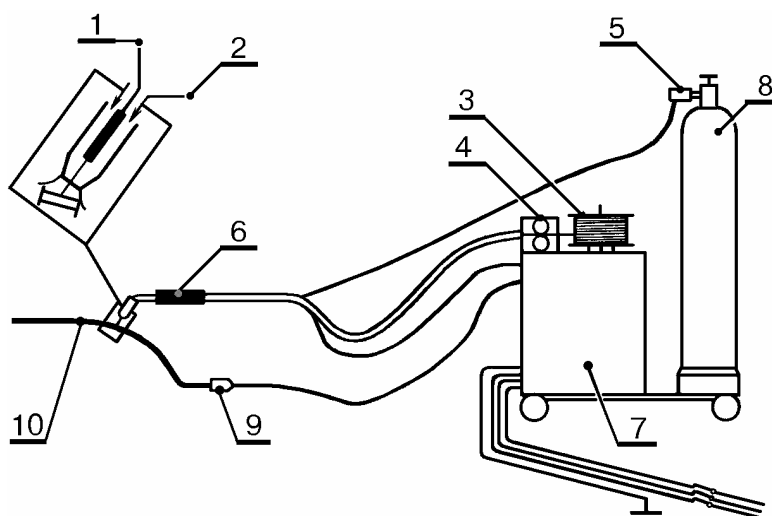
Схема полуавтоматической установки МИГ (металл – инертный газ):
